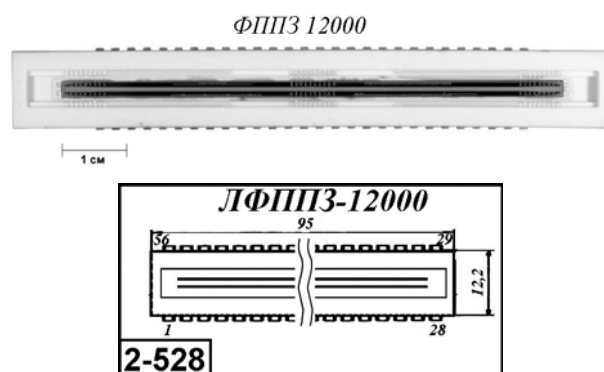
Внешний вид и габаритные размеры ФППЗ 12000Л
